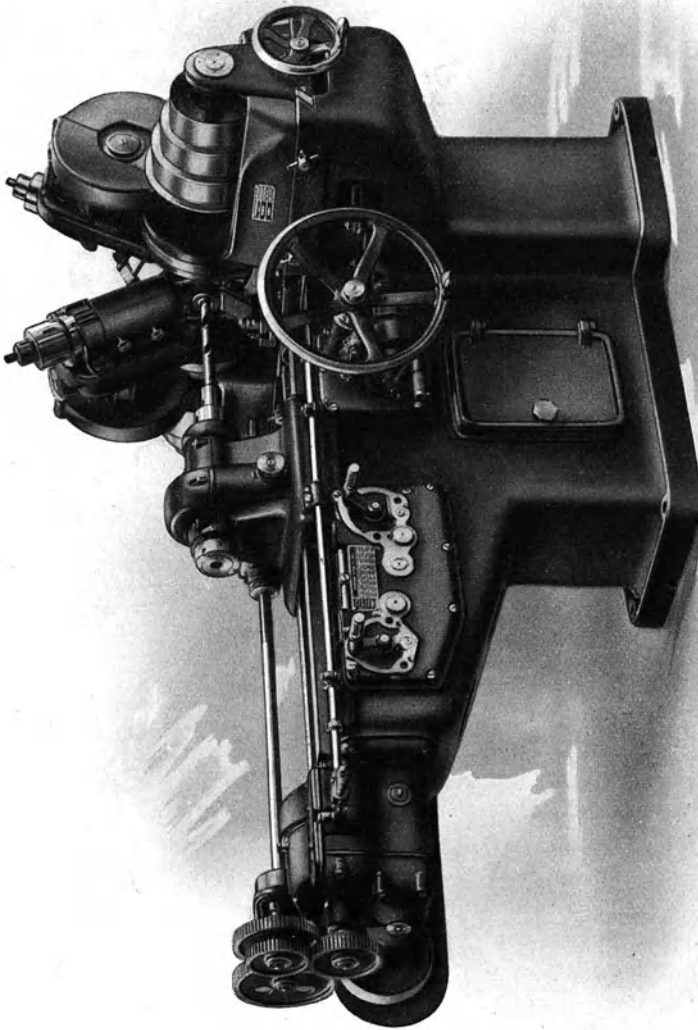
Die Spiralbohrerfräsmaschine von Biernatzki & Co.
